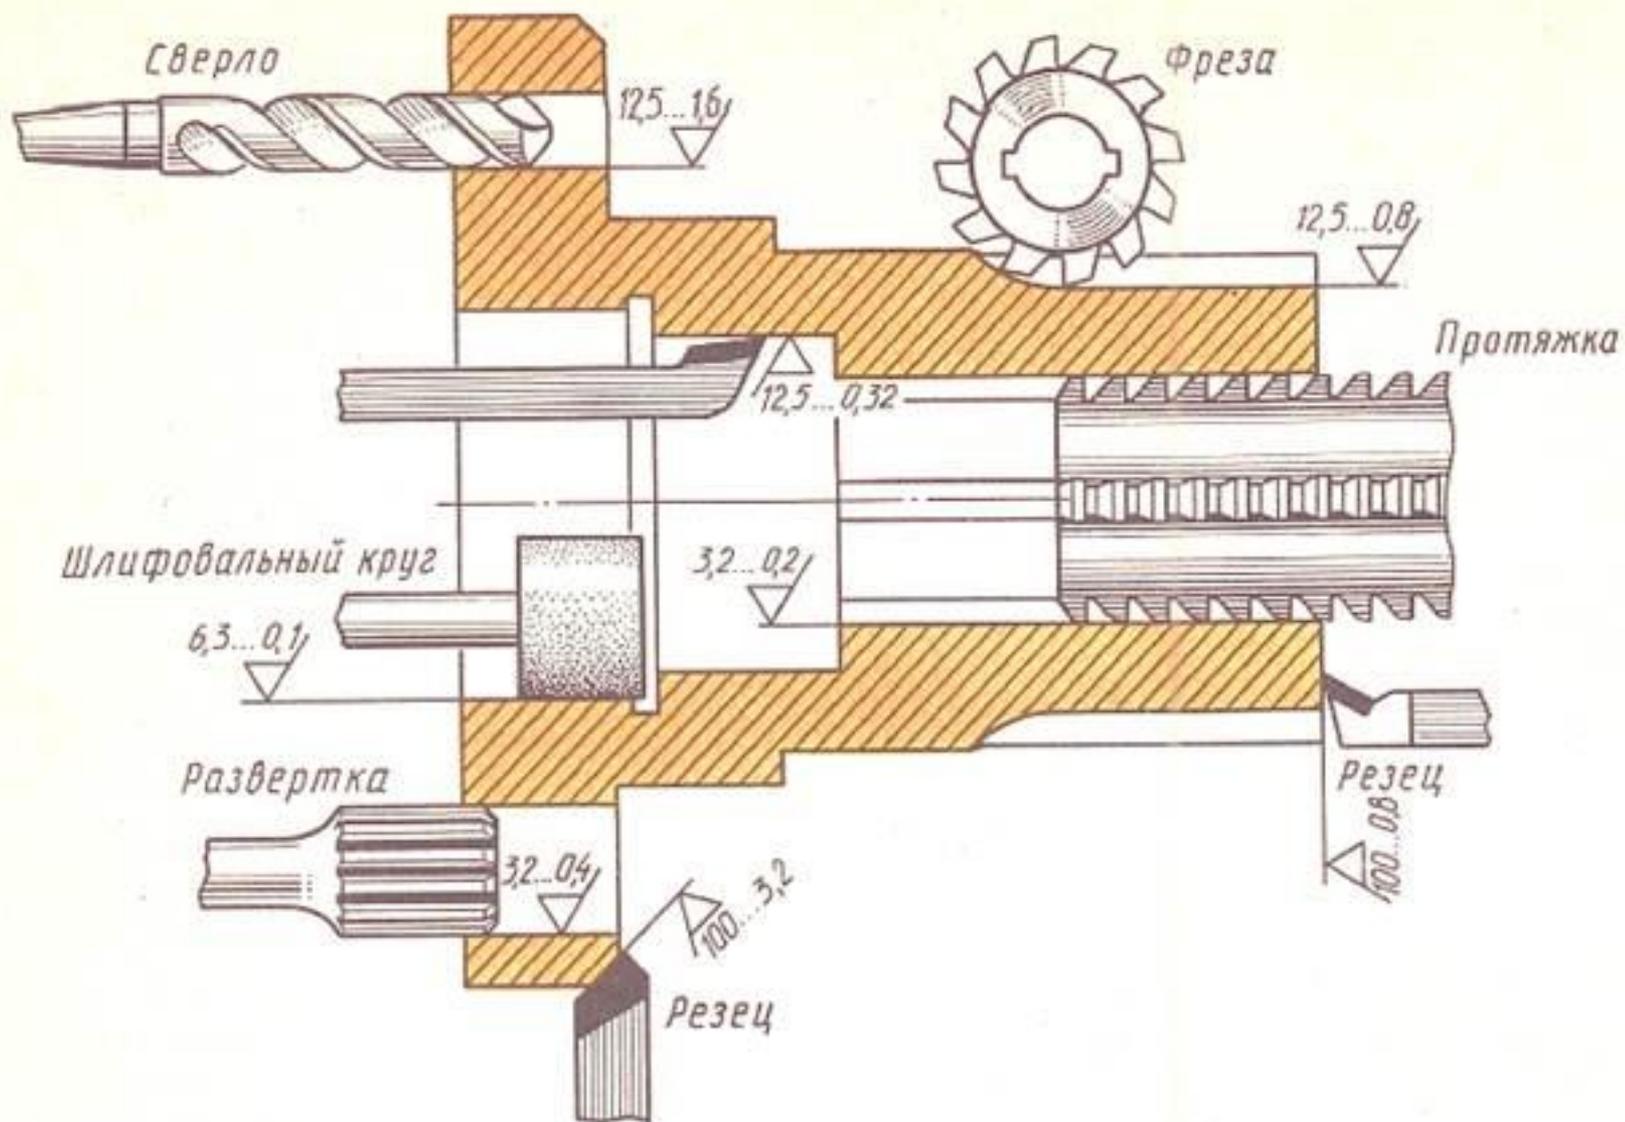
Примерная шероховатость поверхностей, получаемая при обработке различными способами
